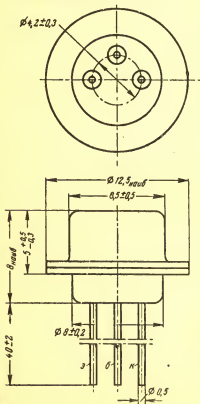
Габаритный чертеж транзисторов П27—П28.
